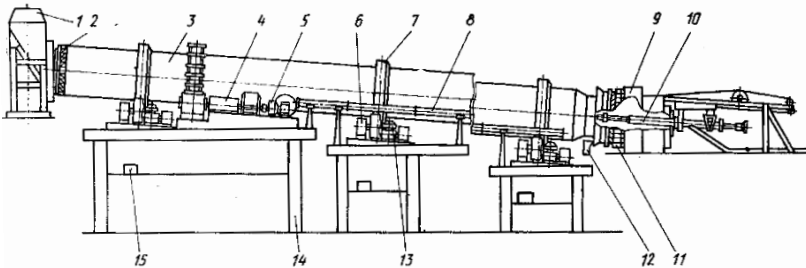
Загальний вигляд короткої обертової печі сухого способу виробництва: 1 – завантажувальна головка печі, 2 та 11 – ущільнення головок печі, 3 – корпус печі, 4 – основні привод корпусу, 5 – допоміжний привод корпусу, 6 – ролюкоопора, 7 – бандаж, 8 – пристрій повітряного охолодження корпусу печі, 9 – розвантажувальна головка печі, 10 – паливна форсунка, 12 – пристрій повітряного охолодження розвантажувальної головки печі, 13 – гідравлічний упор, 14 – залізобетонна опора, 15 – індивідуальна станція для подавання мастильних матеріалів до ролюкоопори.
